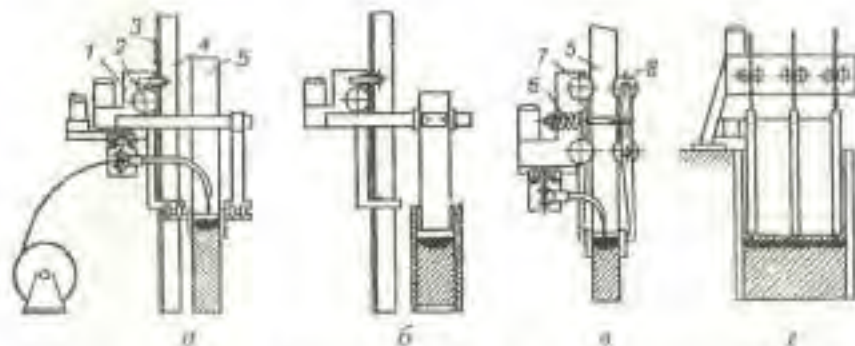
Принципові схеми будови апаратів для електрошлакового зварювання:
